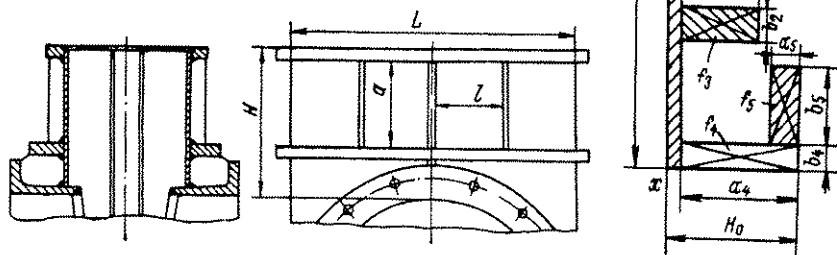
Сварной корпус задвижки большого диаметра прохода
